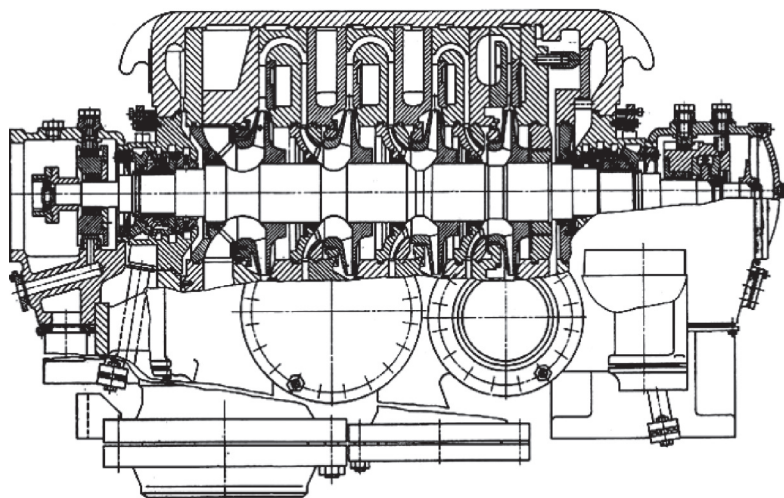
Унифицированный 4-ступенчатый корпус центробежного компрессора СКБК
